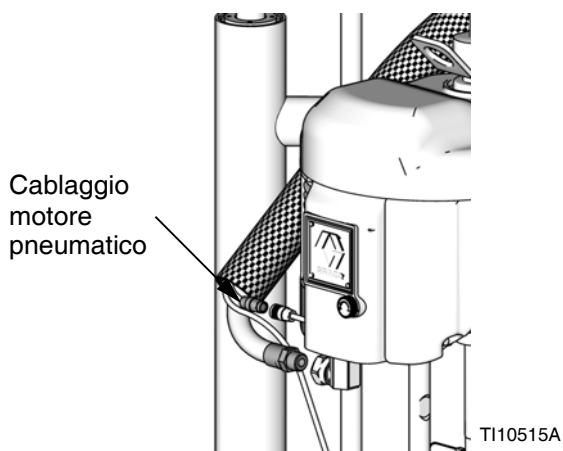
Cablaggio motore pneumatico NXT 2200-6500
